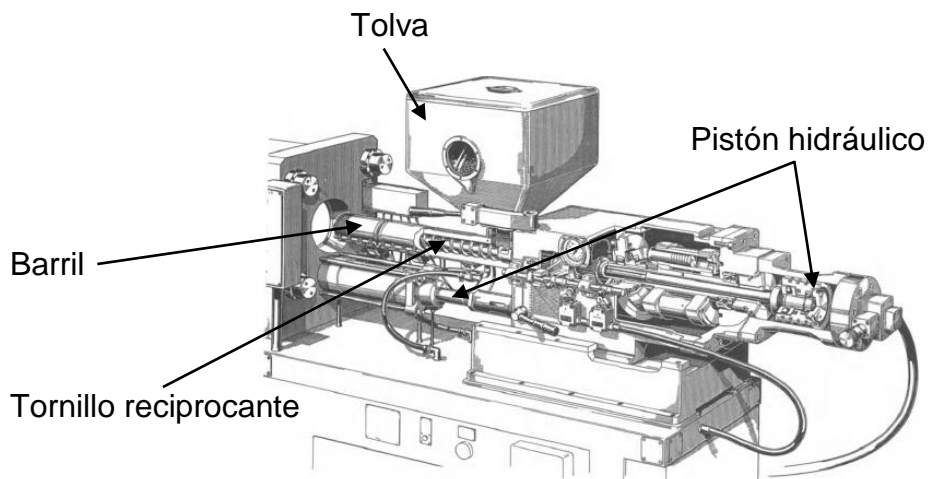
Vista en corte de una máquina de moldeo por inyección [24]
